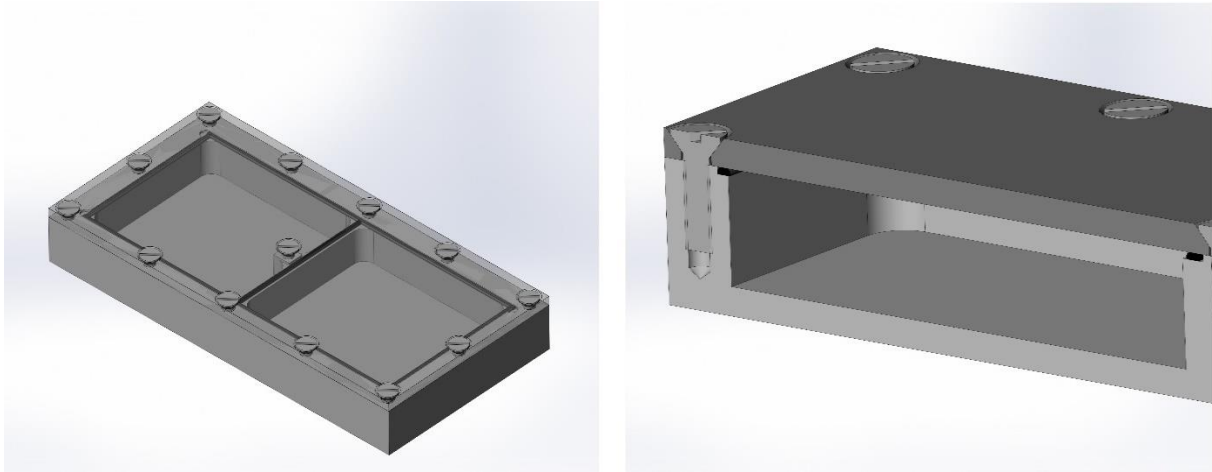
Установка крышки с эластичной ЭМС прокладкой
